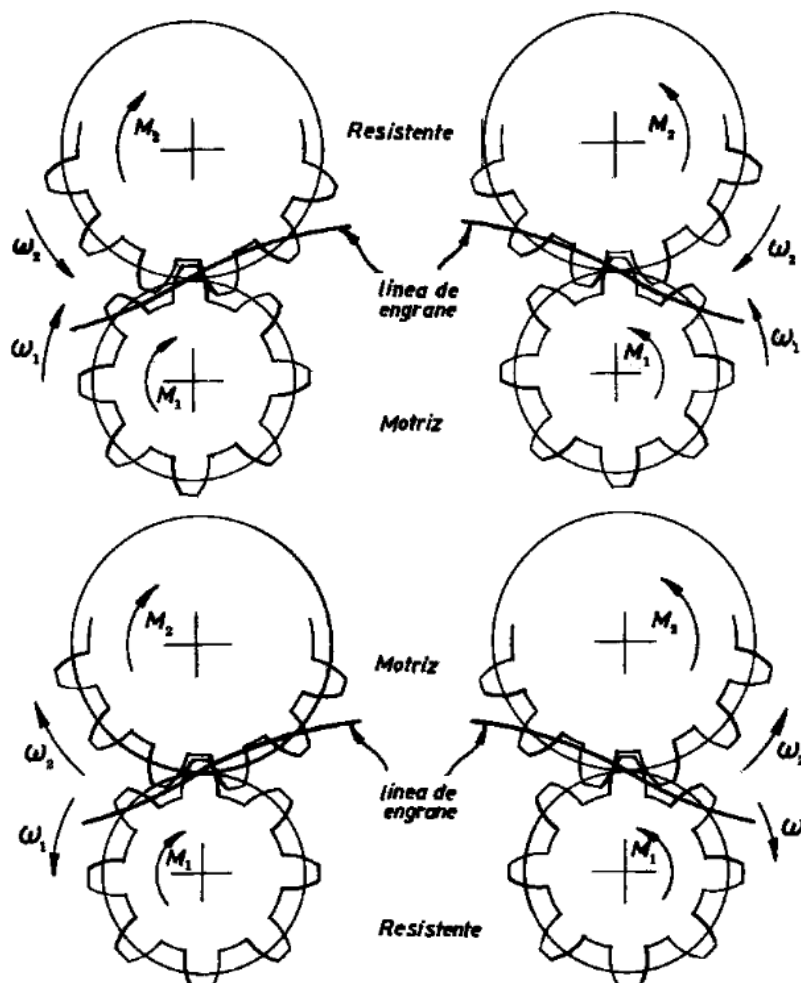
Líneas de engrane de engranajes de perfil de diente cicloidal
